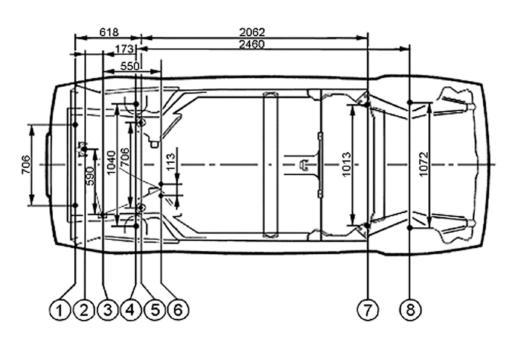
Точки крепления двигателя и подвесок на кузовах 2108; 2109; 21099; 2113; 2114; 2115:
